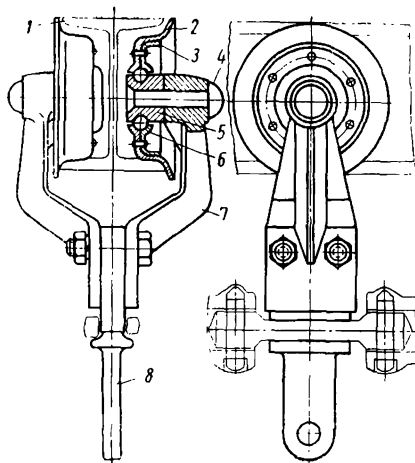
Тележка подвесного конвейера: 1 — двутавровая балка; 2 — ролик; 3 — крышка подшипника; 4 — ось; 5 — втулка; 6 — шарик; 7 — кронштейн; 8 — серьга; 9 — тяговая цепь
